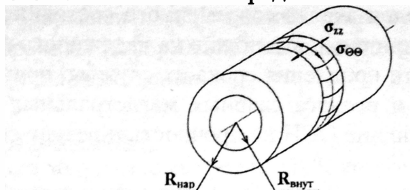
Схема сварного соединения и компоненты напряженного состояния
